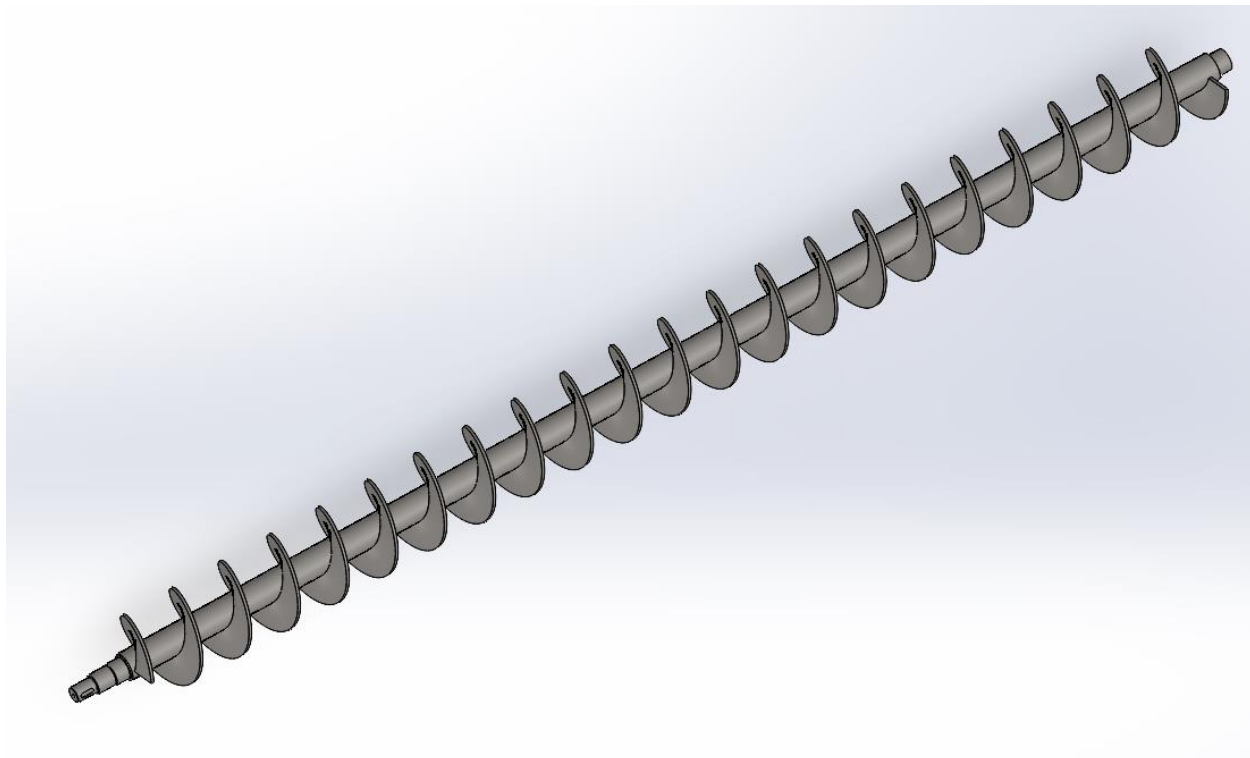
Загальний вигляд змодельованого шнека
